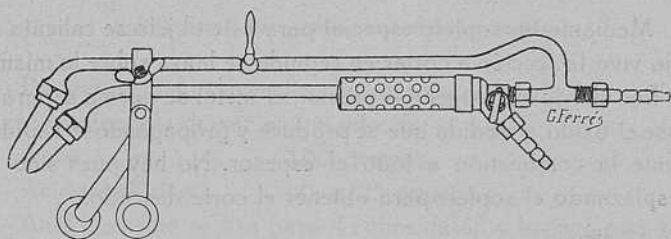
Soplete para cortar, montado sobre ruedas.
